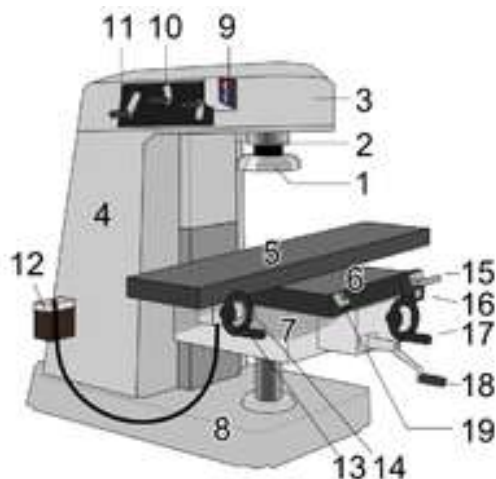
Вертикально-фрезерный станок (1 — фреза, 2 — шпиндель, 3 — хобот, 4 — станина, 5 — стол, 6 — салазки, 7 — консоль, 8 — фундаментная плита)
